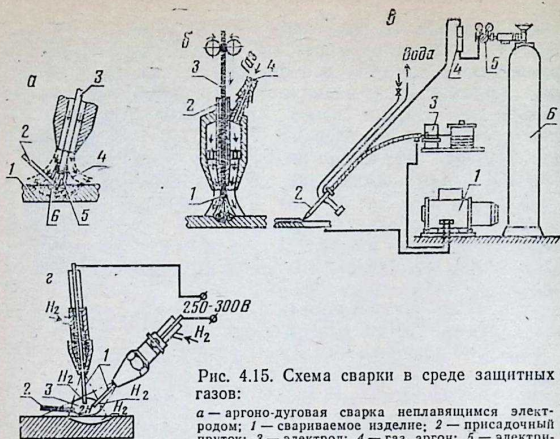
Схема сварки в среде защитных газов:
